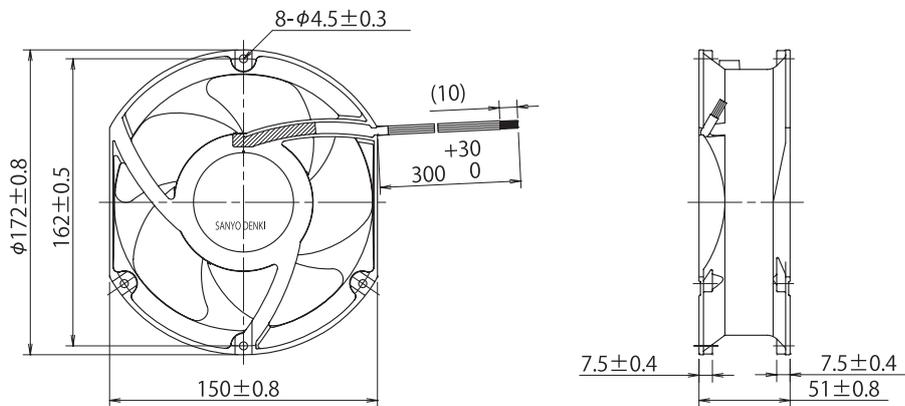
「San Ace 172W」WGタイプの寸法諸元 (単位: mm)
